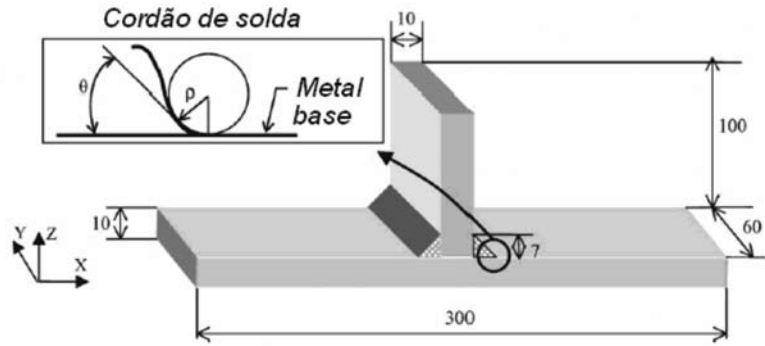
Geometria das juntas soldadas em T (mm) [22]
